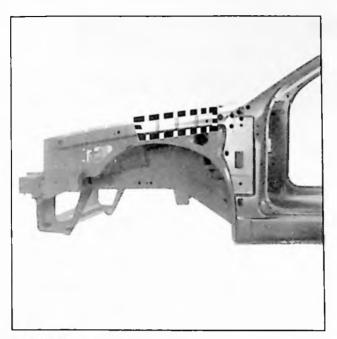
C Souder par points électriques. Souder par points "bouchon" MAG. Meuler les points de soudure MAG.
